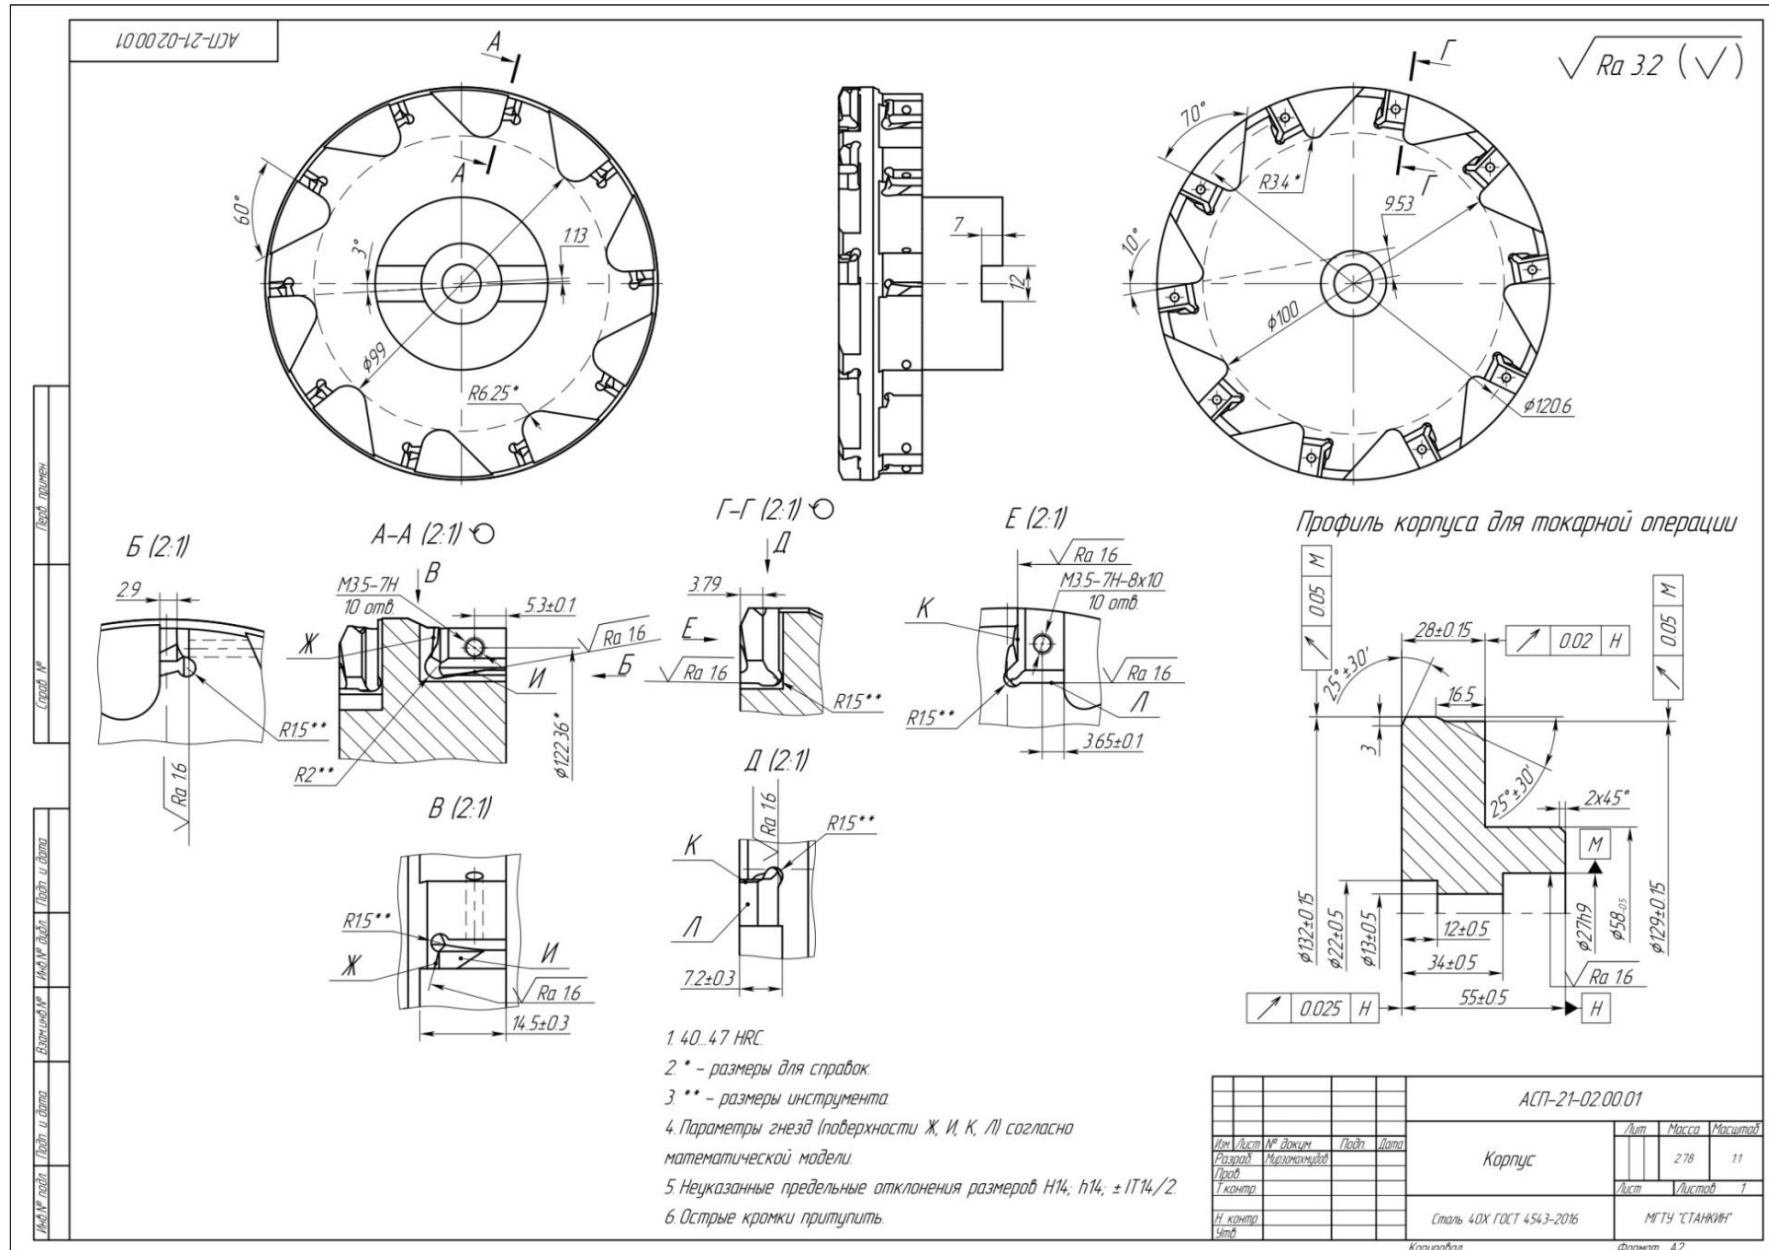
Рабочий чертеж корпуса разработанной конструкции дисковой фрезы с СМП.
